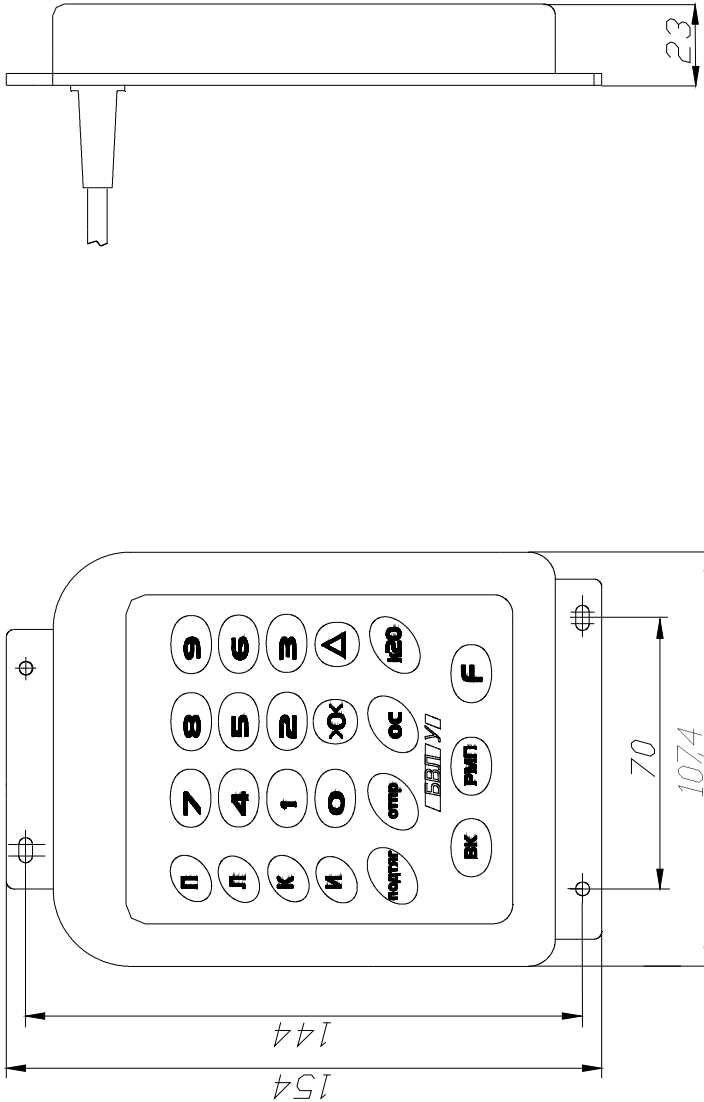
Внешний вид и габаритные размеры БВЛ-У 36991-370-00-01
